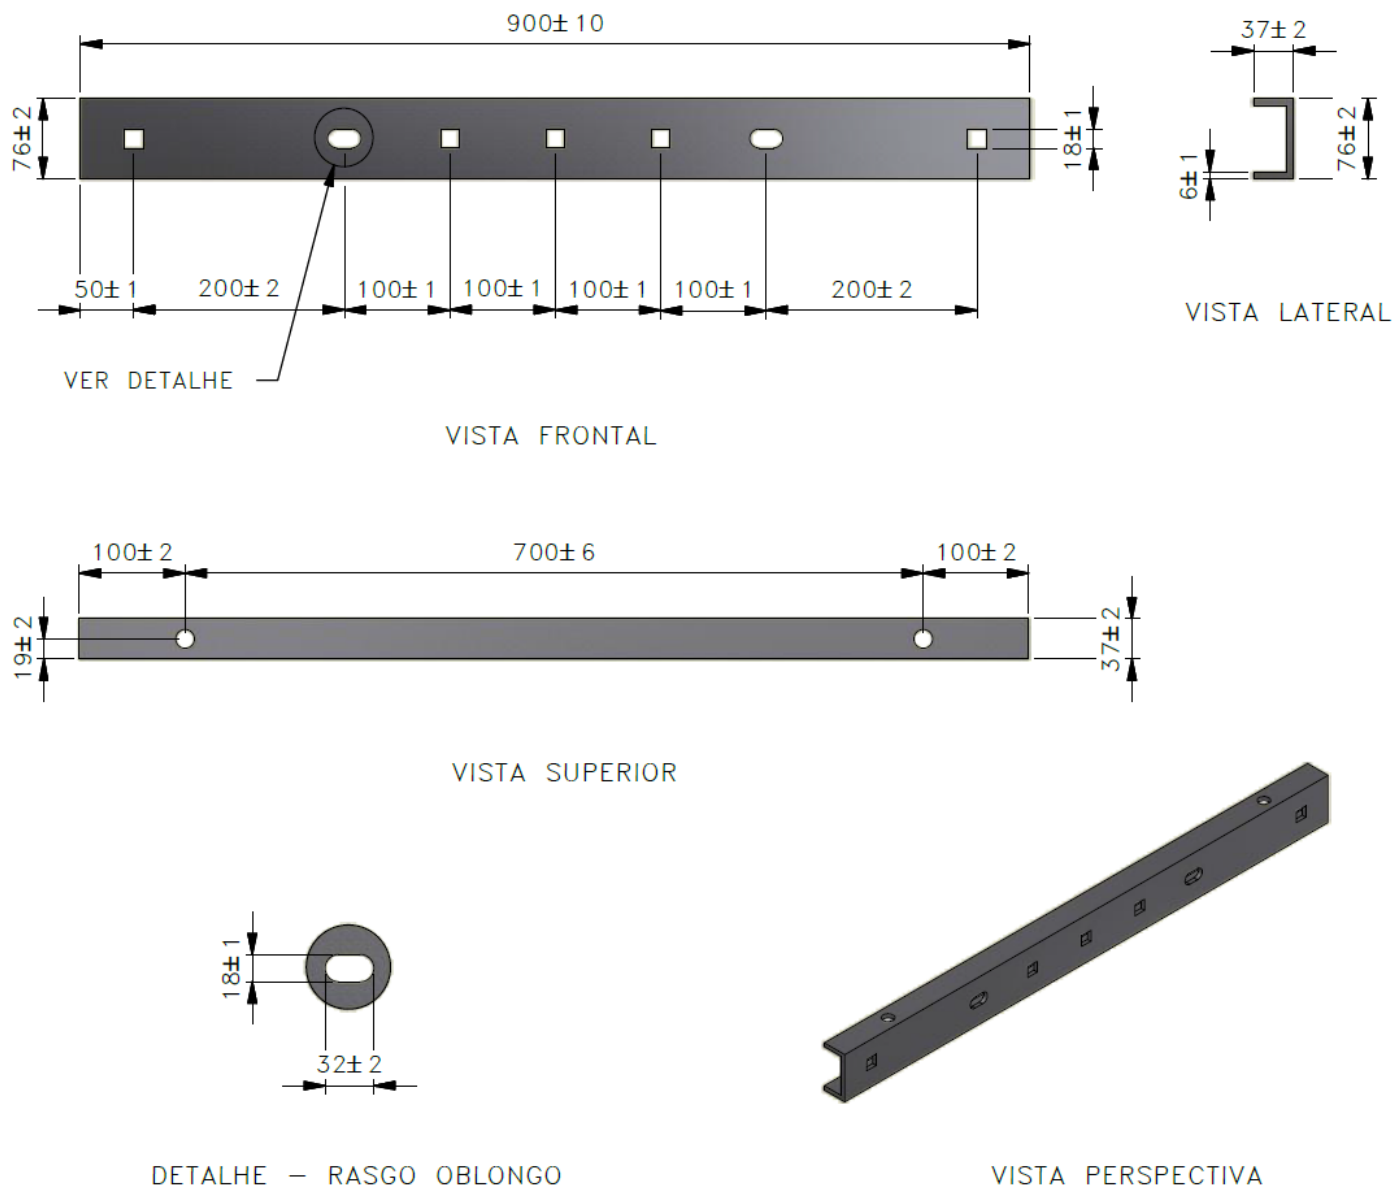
VISTAS E DETALHE DO PERFIL U
